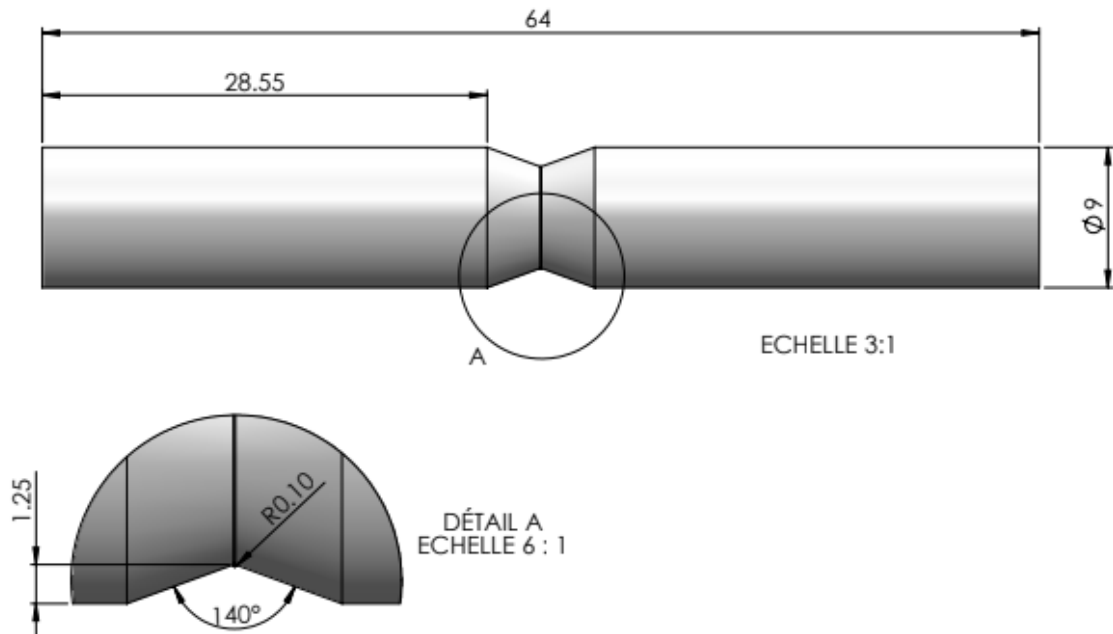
Géométrie et dimension de l'éprouvette V140R0.1
